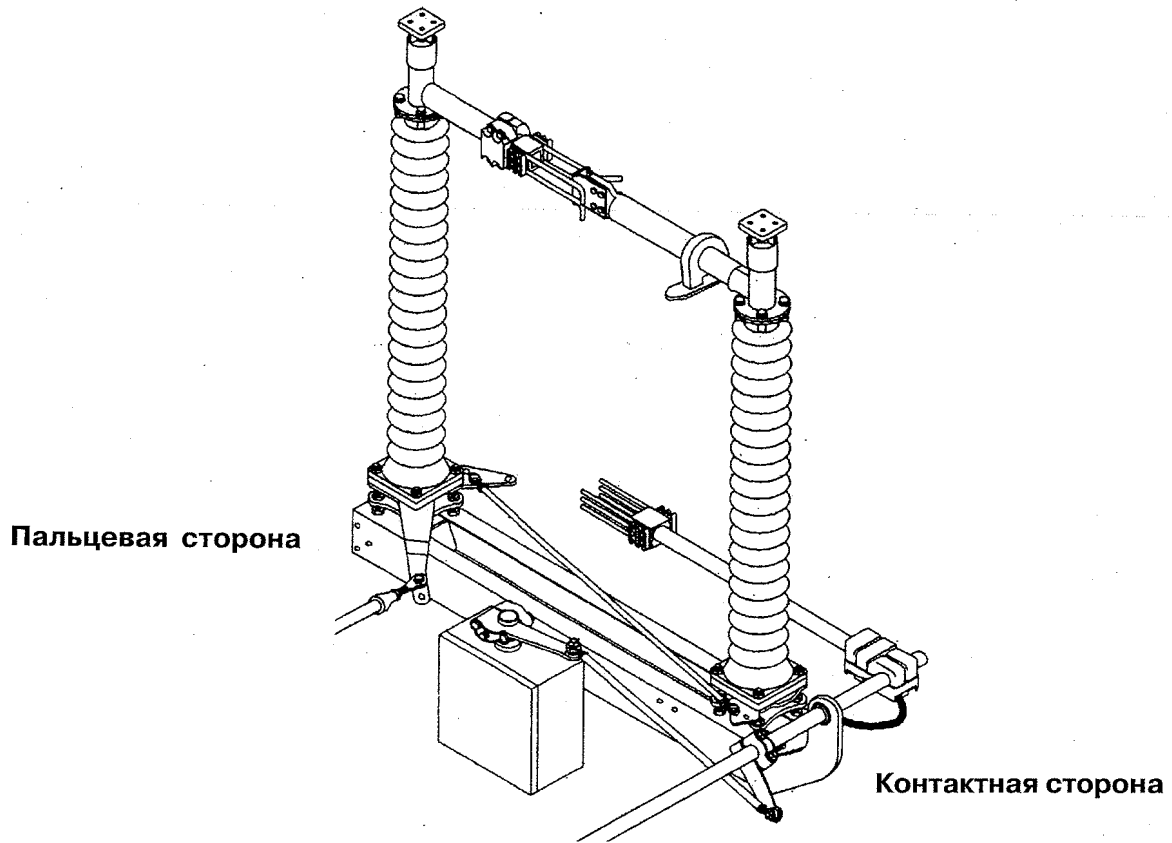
Установка приводного механизма заземлителя. Установка на раме
